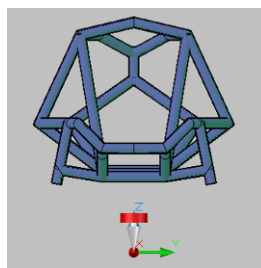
Representación en alzado de la estructura 1.0.
